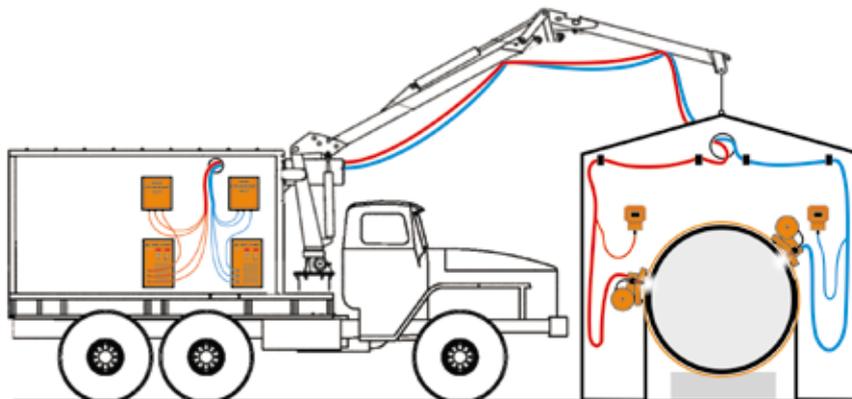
Схема расположения сварочной установки УАСТ-1 в кунге и палатке
